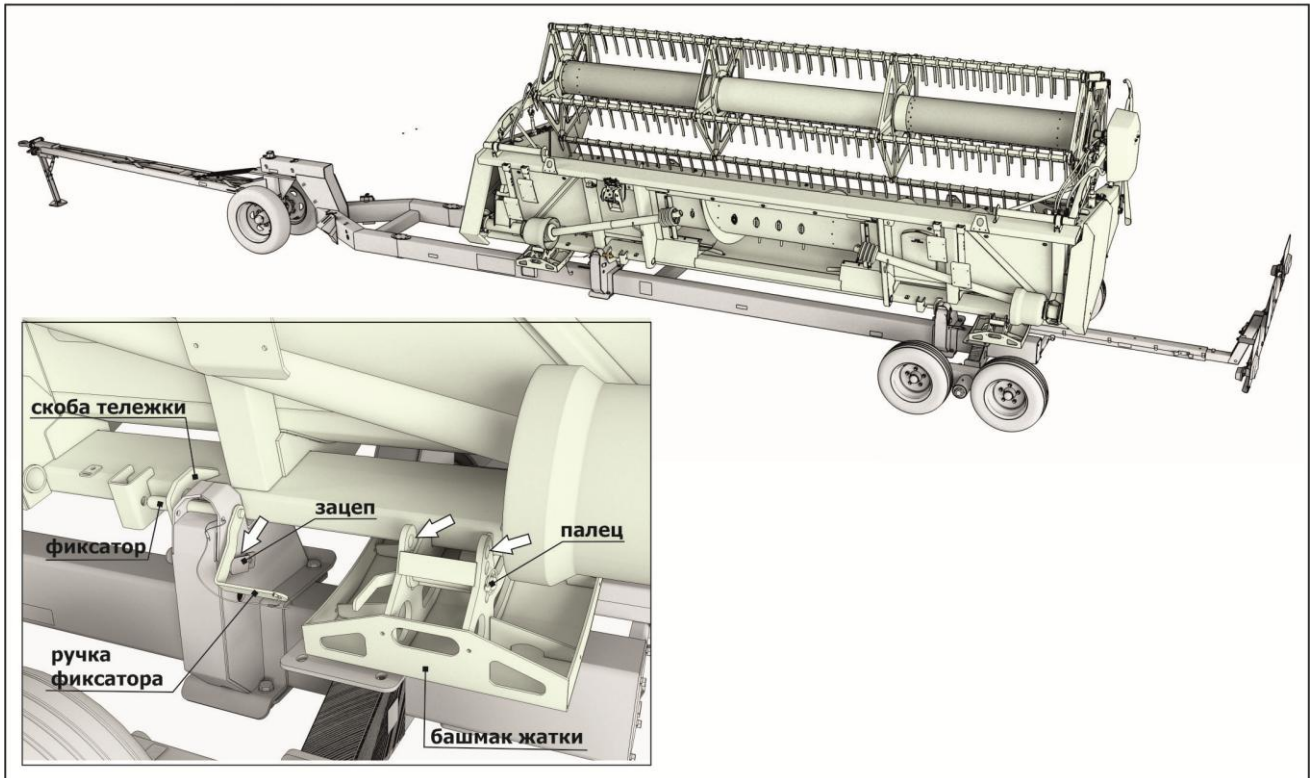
Установка жатки на приспособление ППА-4000-01
